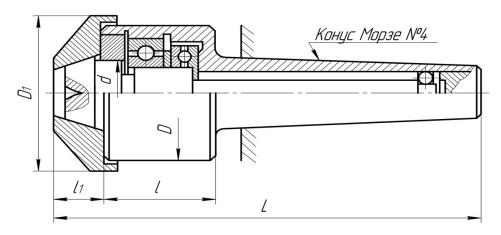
Задний грибковый вращающийся центр для обработки полых заготовок
